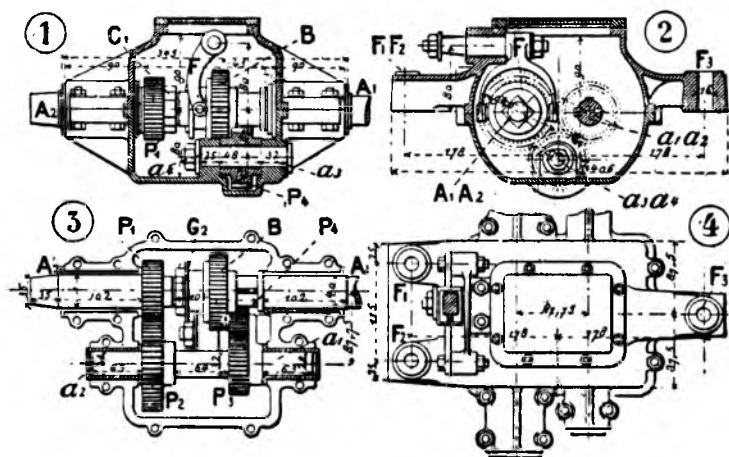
Механизм перемены вращения винта посредством перестановки зубчаток. — A_1 , конец коленчатого вала двигателя. — A_2 , конец гребного вала, — a_1, a_2 , вторая передаточная ось с насаженными на нее зубчатками P_2 и P_3 — a_3, a_4 , третья передаточная ось, расположенная внизу, с насаженной на нее зубчаткой P_4 . — G_2 , передвижная втулка с механизмом прямого соединения (слева) и зубчаткой B . — F , вилка для перестановки зубчатки. — F_{1-2} , лапы для прикрепления коробки. Размеры показаны в мм. Черт. 1 — вид сбоку по длине оси; Черт. 2 — разрез поперечный; Черт. 3 — план. Черт. 4 — вид закрытой коробки сверху.
